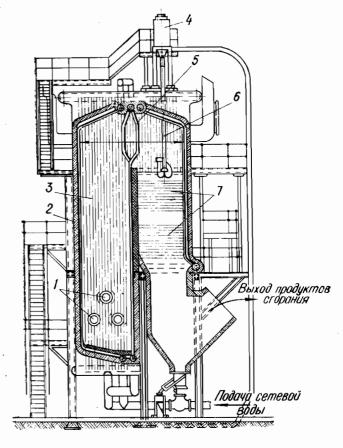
Водогрейный котел ПТВМ-3ОМ: I— газомазутные горелки; 2— каркас; 3— топочная камера; 4— дробеочистительное устройство; 5— фестон; 6— поворотная камера; 7— 3 меевики.
